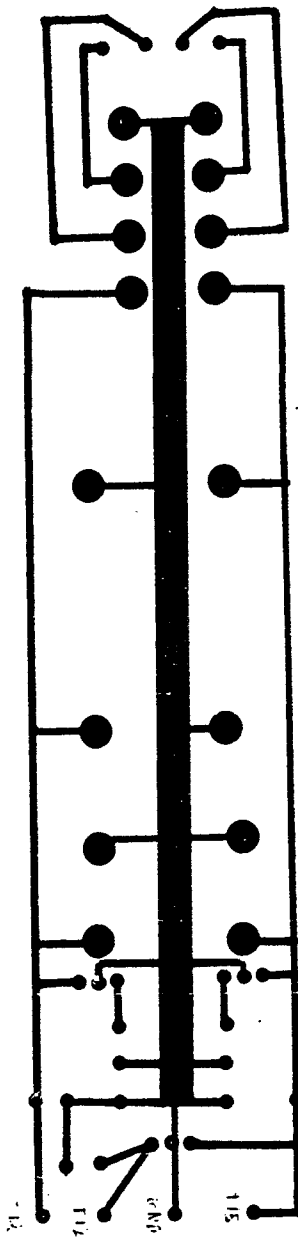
Dibujo de la placa de circuito impreso que fue diseñada para la fuente de alimentación.
